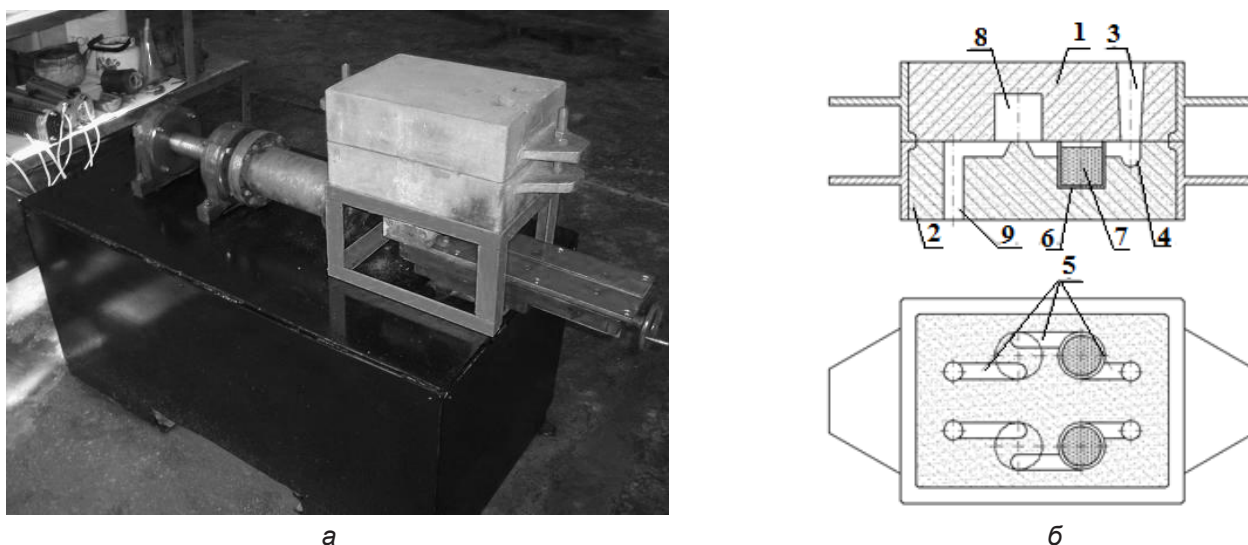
Общий вид установки центробежного литья для изготовления отливок с дифференцированными свойствами (а) и схема заливочно-модифицирующего устройства (б): 1 – верхняя полуформа; 2 – нижняя полуформа; 3 – стояк; 4 – зумпф; 5 – горизонтальные каналы; 6 – реакционная камера; 7 – модификатор; 8 – шлакоуловитель; 9 – вертикальный выходной канал
